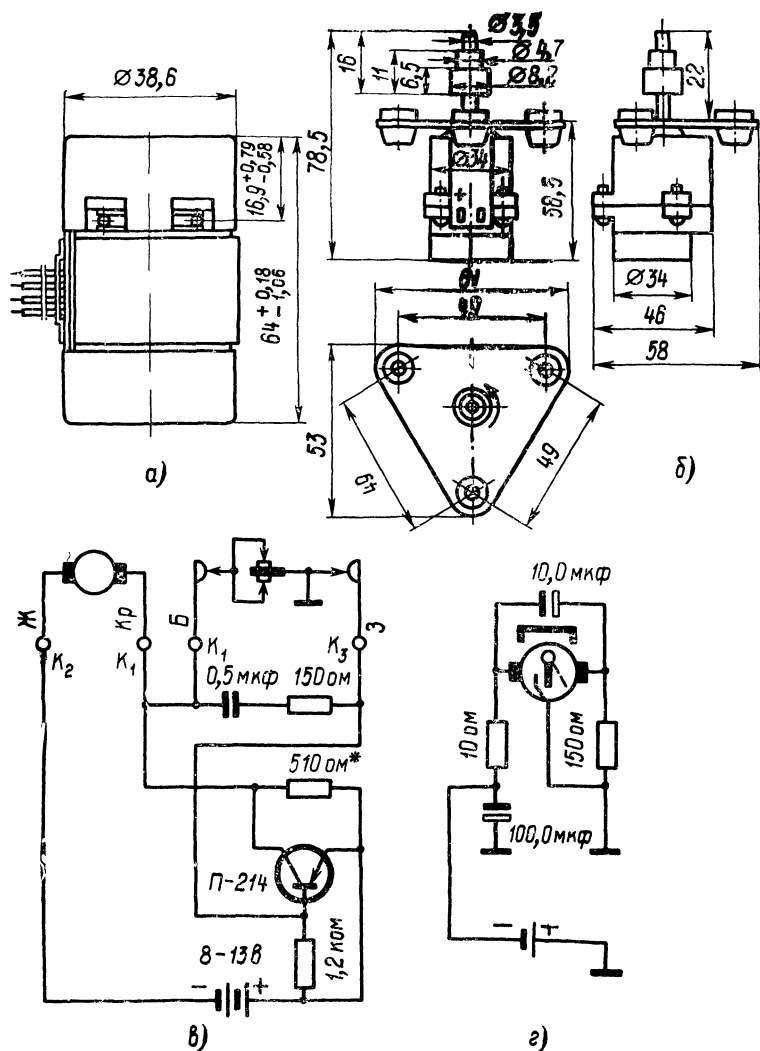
Габаритные чертежи и схемы включения коллекторных двигателей ДКС и ДРВ-0,1.
